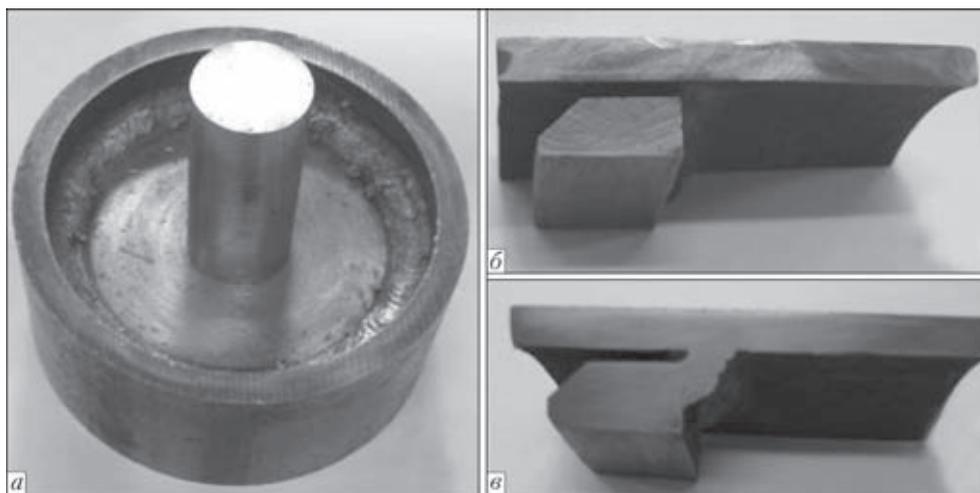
Результаты приварки доньшка к внутренней поверхности трубы: *а* — кольцевой шов с перекрытием; *б* — реальный зазор между доньшком и трубой; *в* — форма сварного соединения
